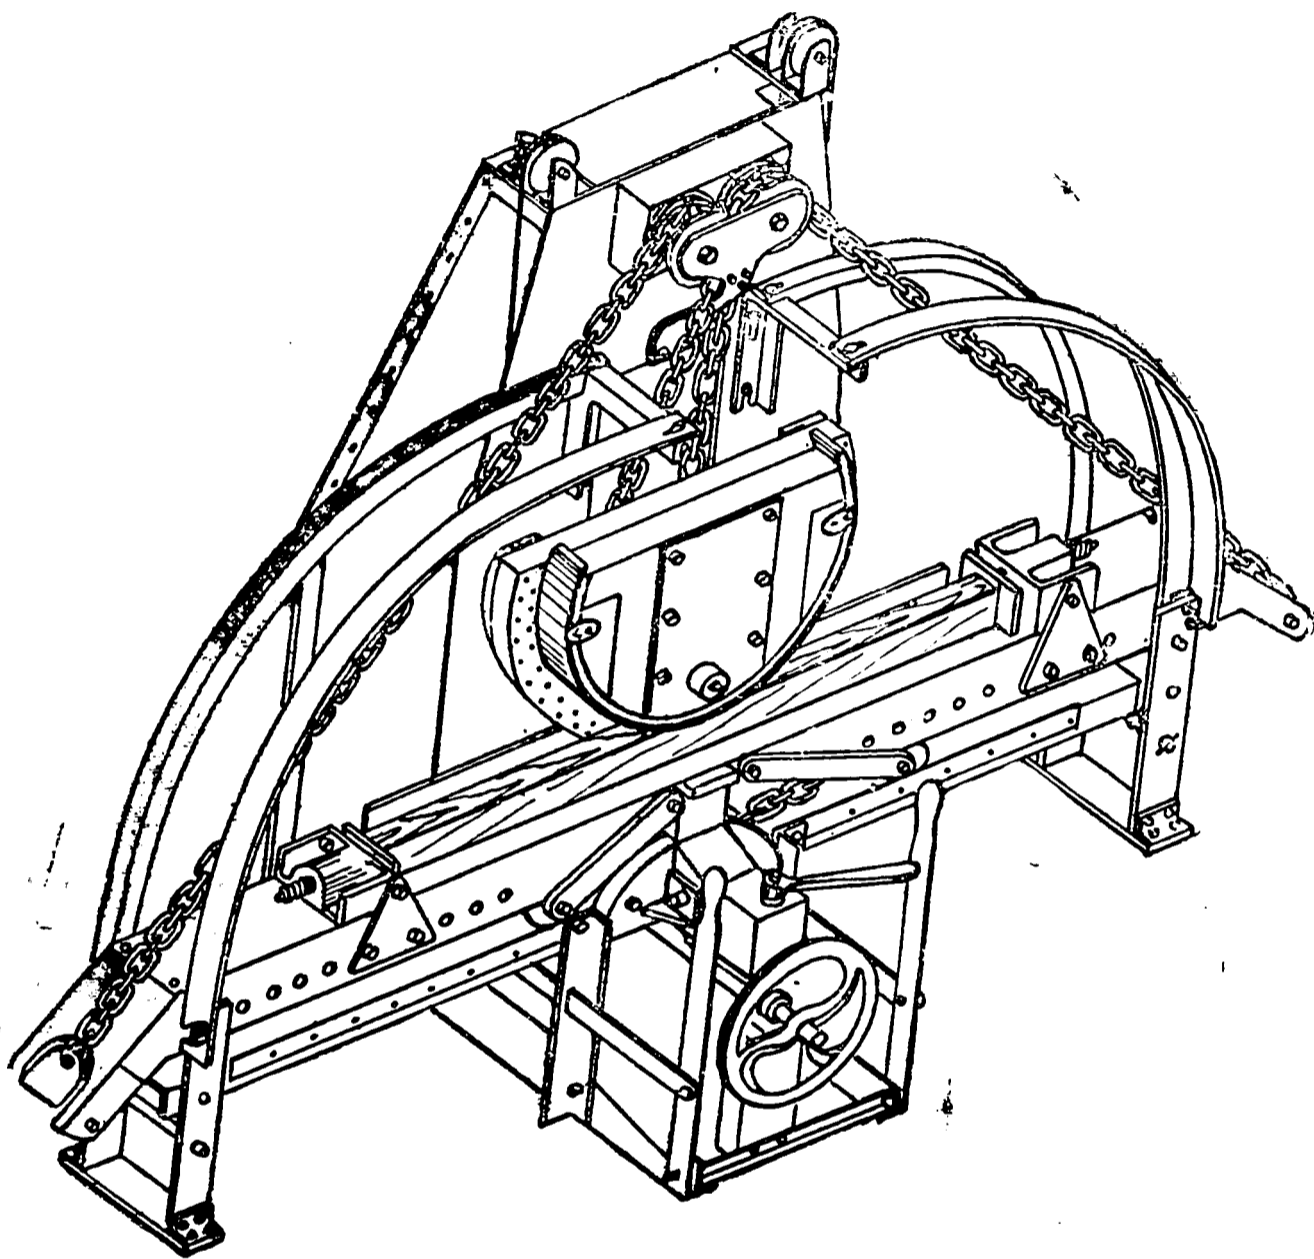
Общий вид вертикального гнутарного станка для гнутья хвойных полуободьев
